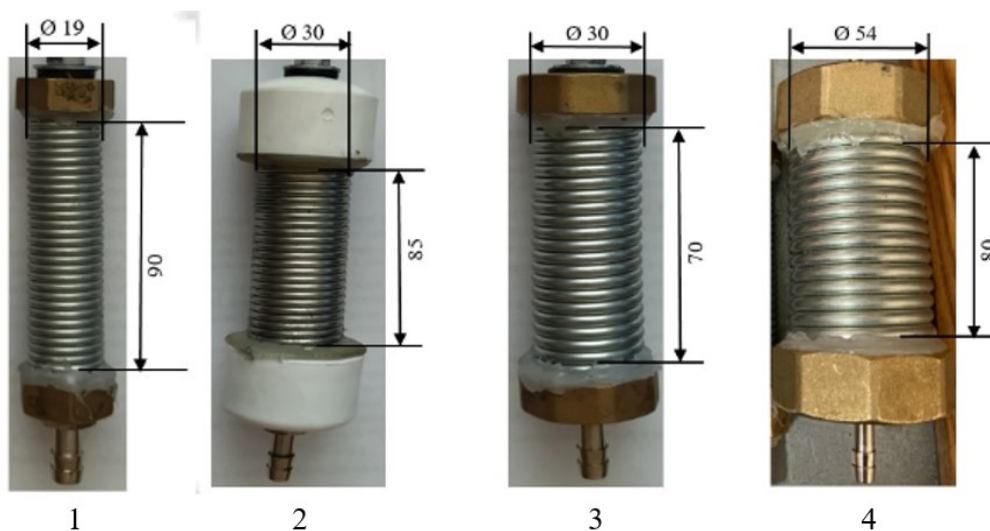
Типоразмерный ряд пружинных диспергаторов воздуха
